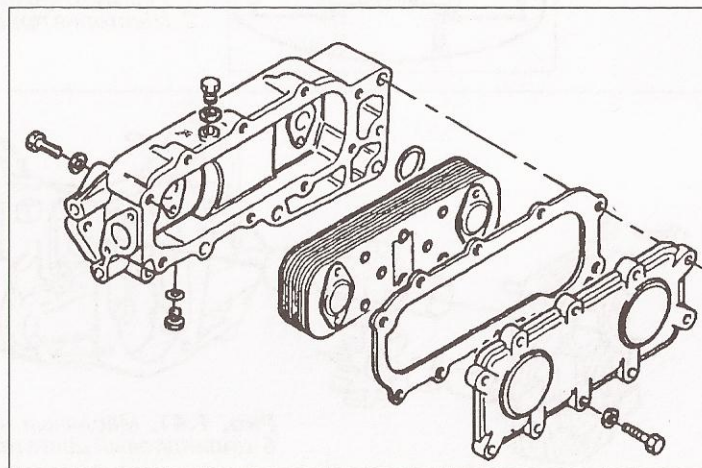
Теплообменник 6-цилиндрового двигателя
